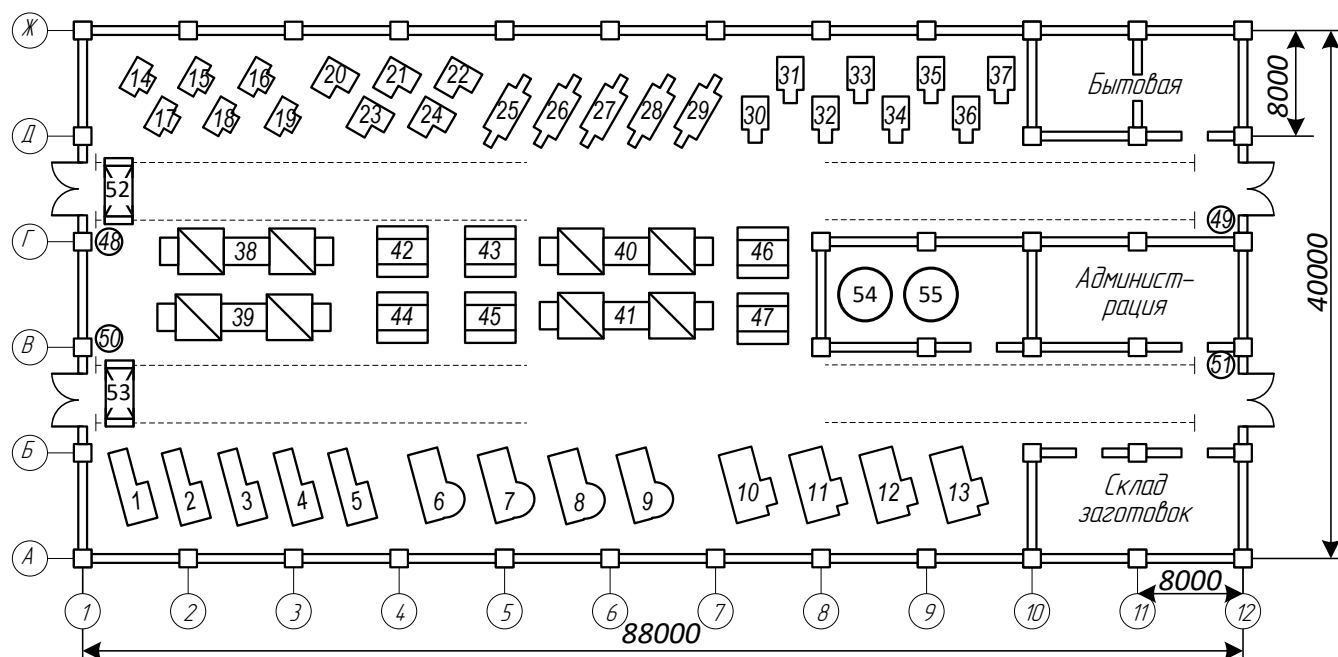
Схема расположения ЭО в цехе металлорежущих станков
